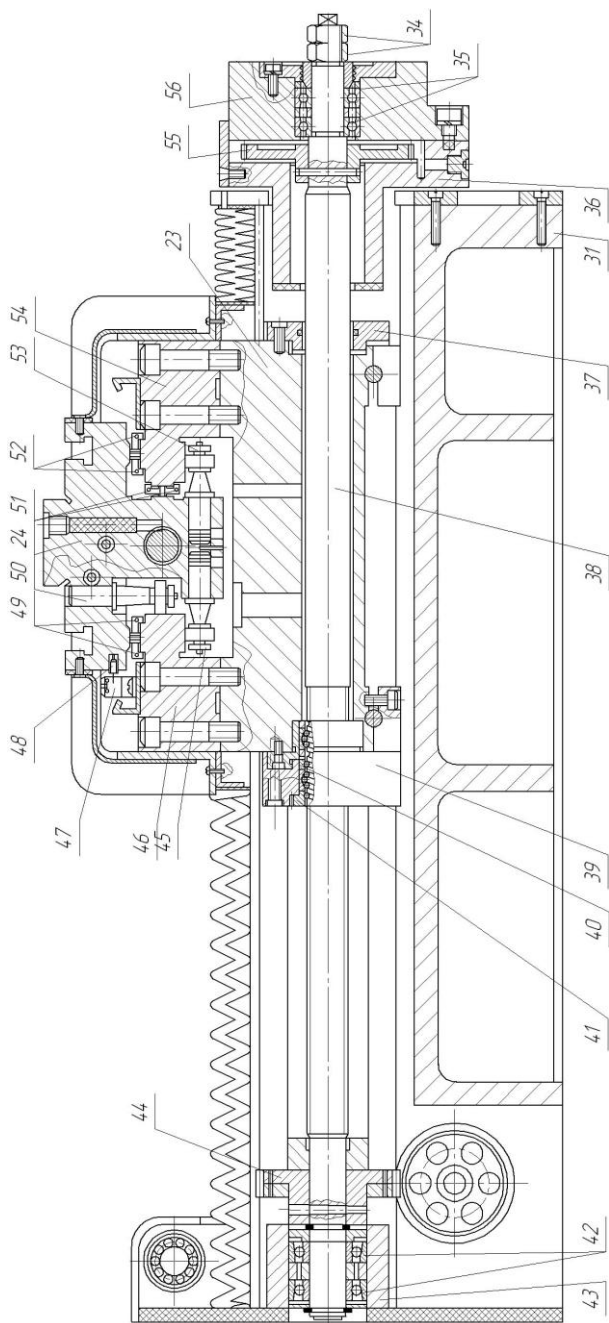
Двухкоординатный суппорт (ось Z) станка мод. ТПК-125В
